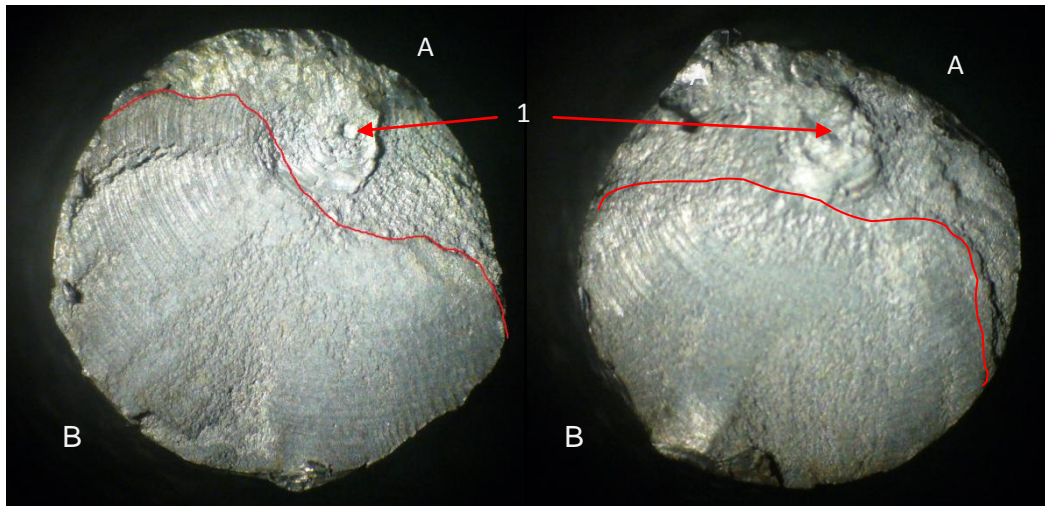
MACROFRACTOGRAFÍA DE SUPERFICIE DE FRACTURA
